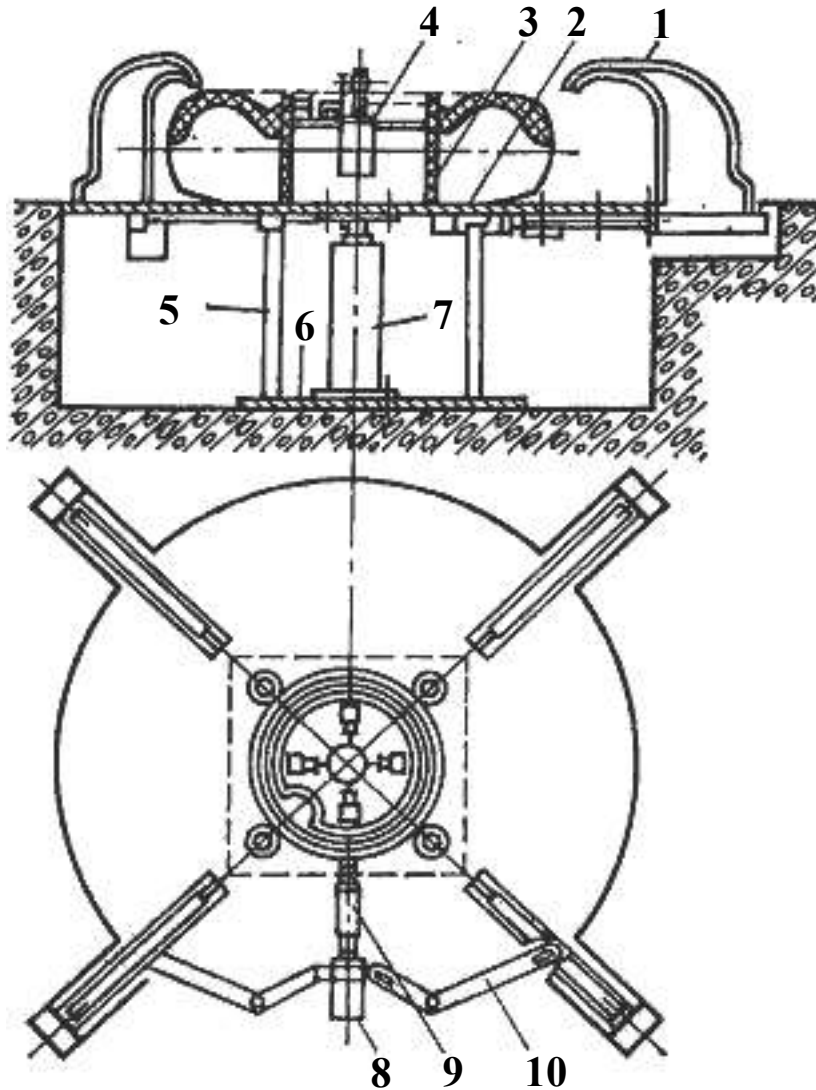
Стенд для сборки и разборки колес автомобилей БелАЗ-548А:
